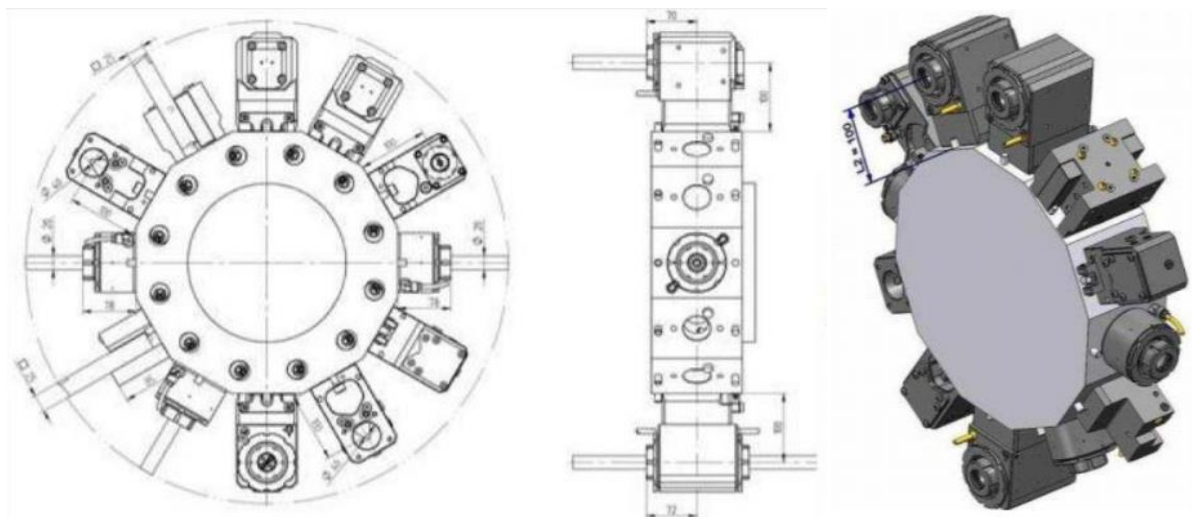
Револьверная головка VDI с державками для токарного и приводного инструмента.
